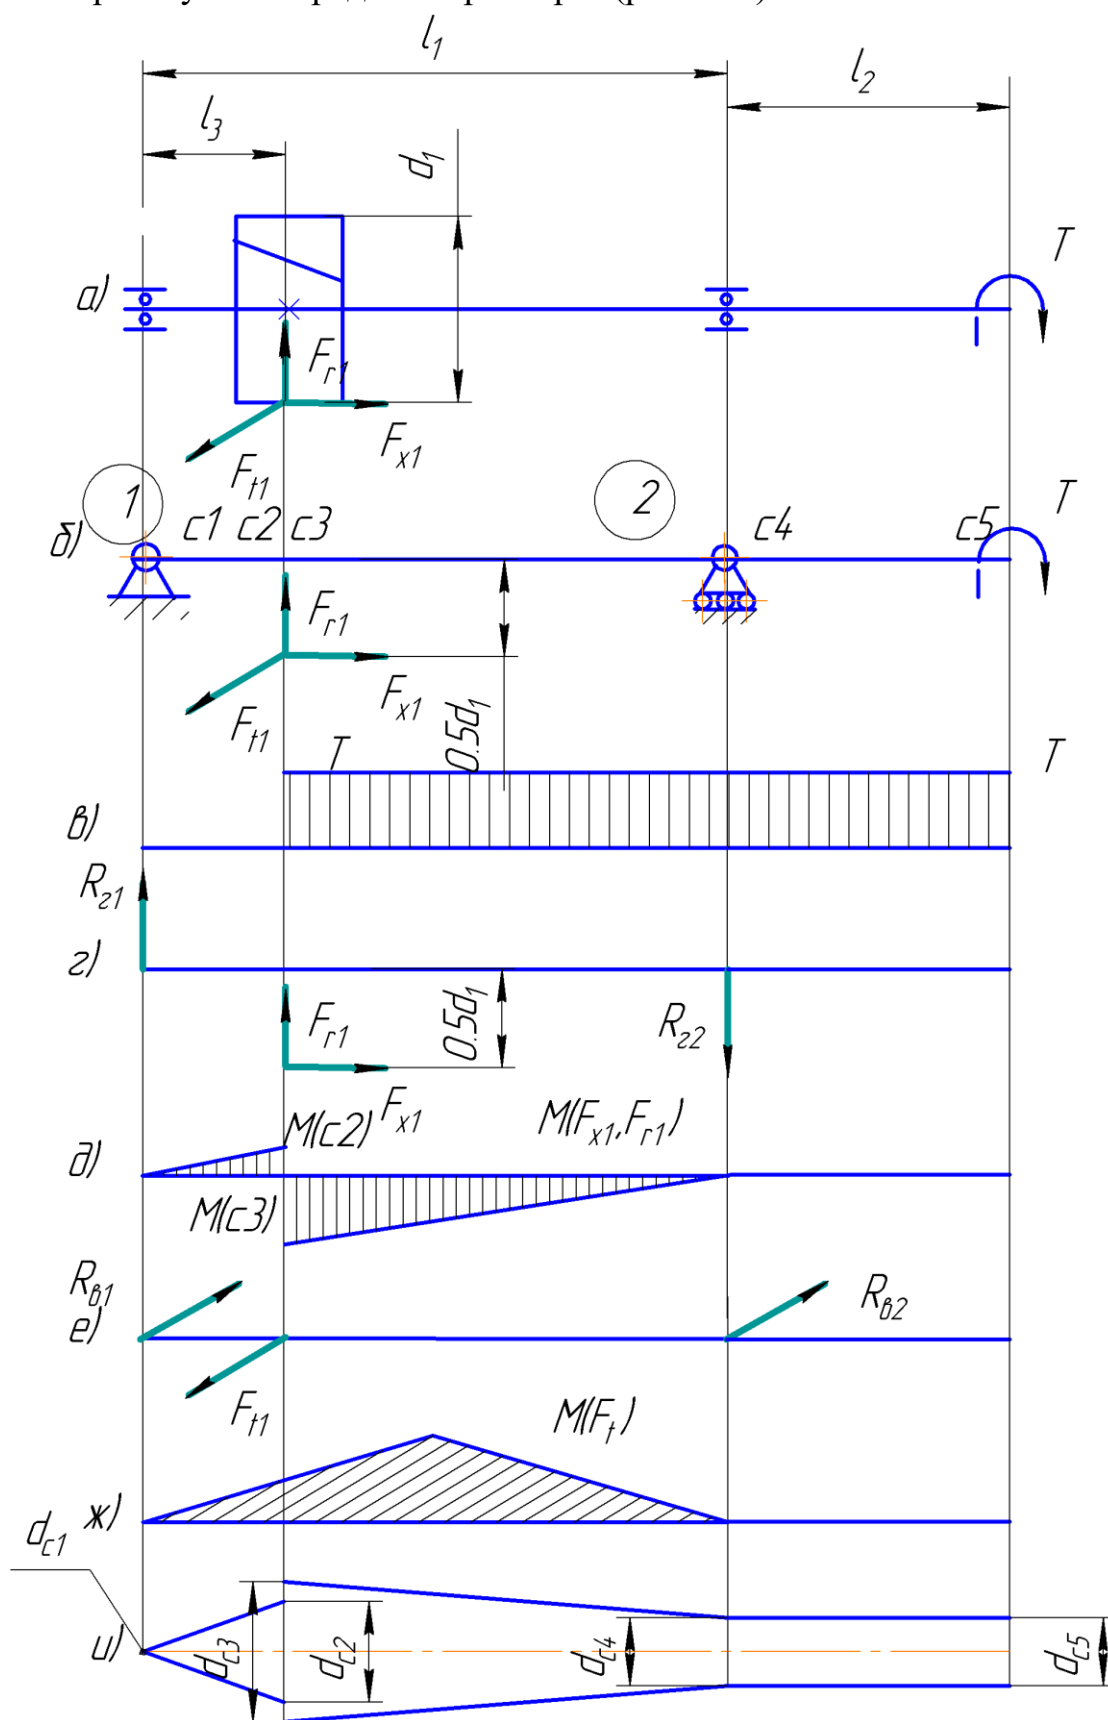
Эпюры вращающего и изгибающих моментов и теоретический профиль ведущего вала редуктора
